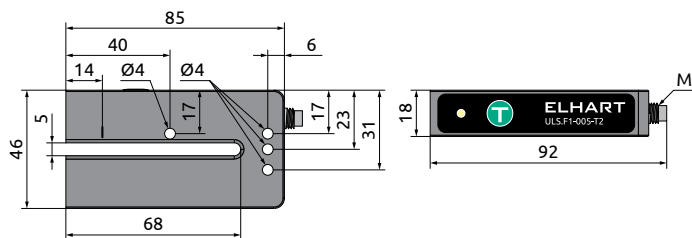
Габаритные размеры ULS.F1-005-T2
